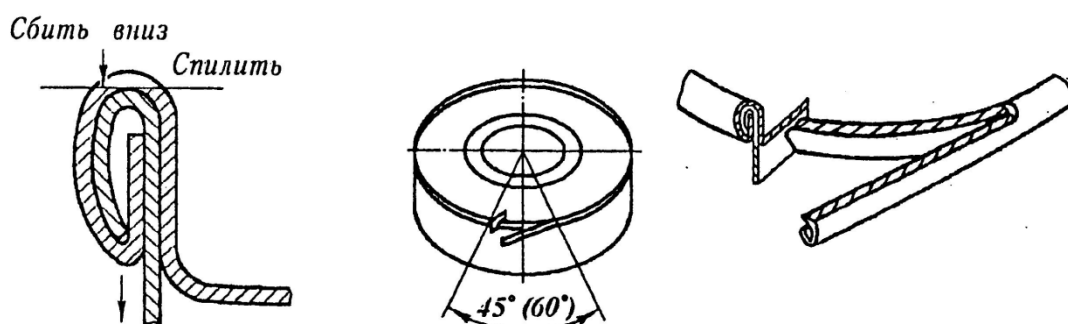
Опиловка Рисунок 10. Общий вид вскрытого шва двойного закаточного шва
